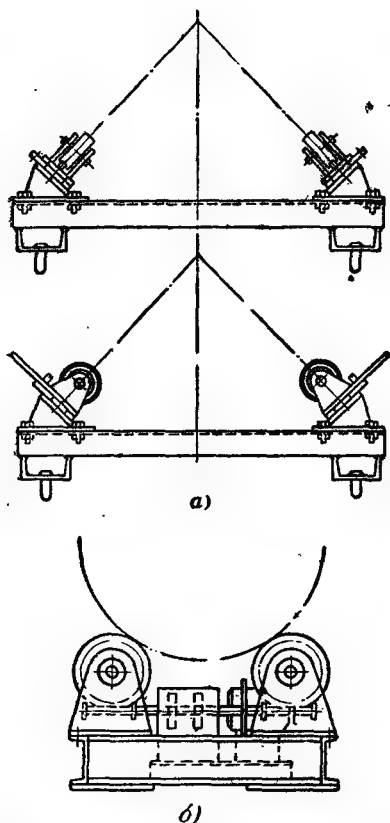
Роликовые кантователи для сборки и сварки цилиндрических обечаек.
